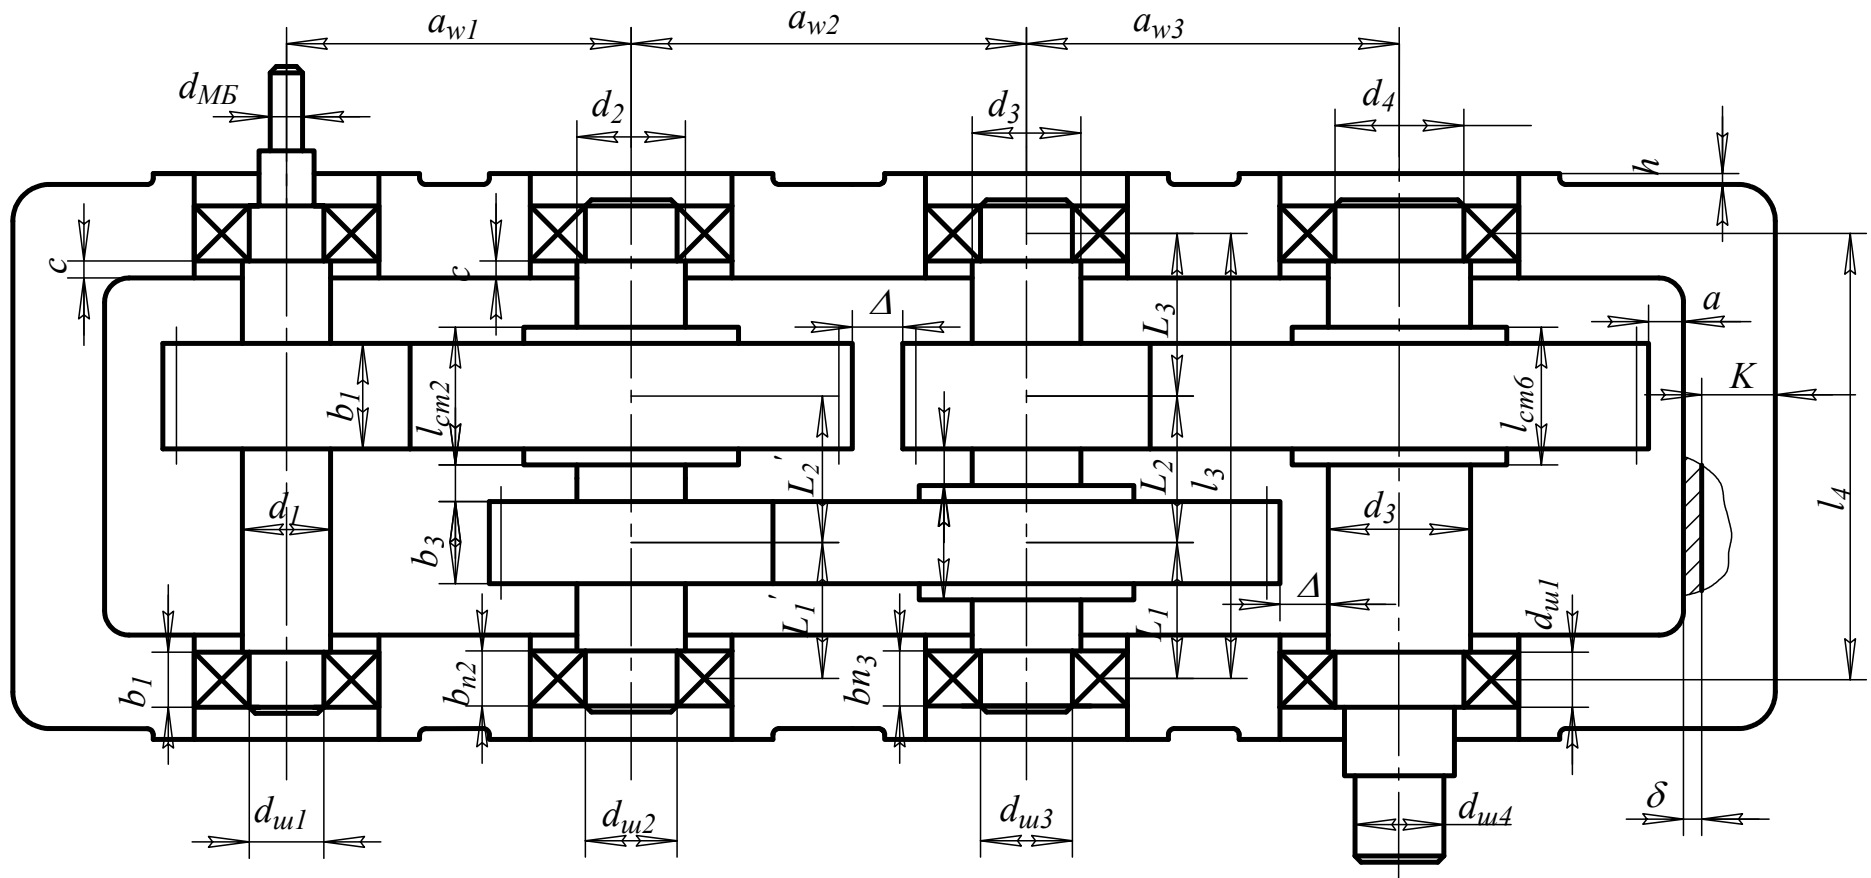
Ескізне компоунвання трьохступеневого циліндричного редуктора
